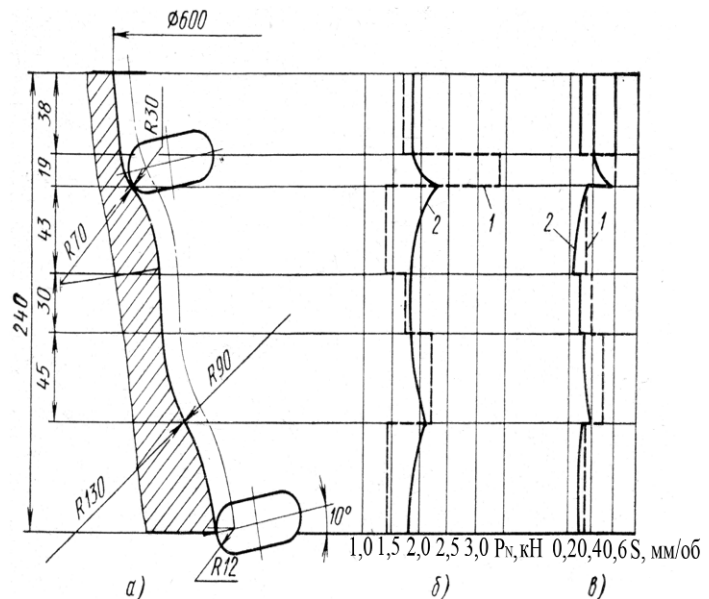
Схема обкатування і епюра зусиль при обкатуванні складної циліндричної поверхні
